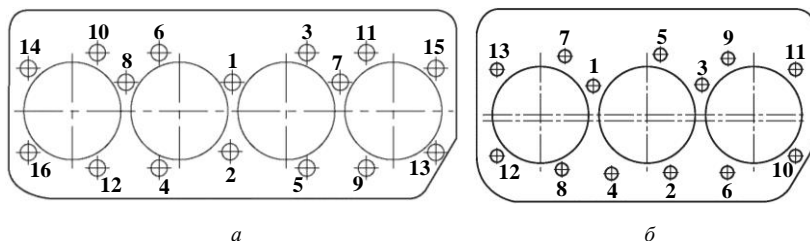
Схема затяжки болтов головки блока цилиндров двигателей Д-243, Д-245 (а) и Д-260 (б)
